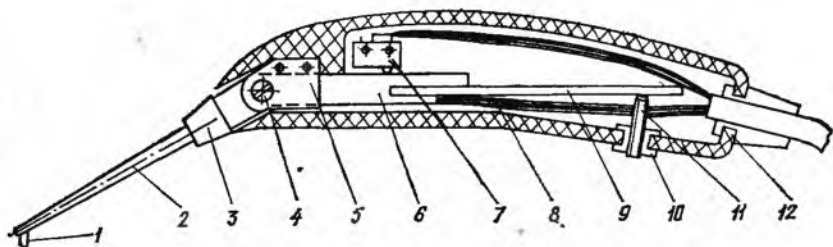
Кинематическая схема пружинного механизма сжатия электродов с ручным приводом для сварки в монтажных условиях (карандаш).
